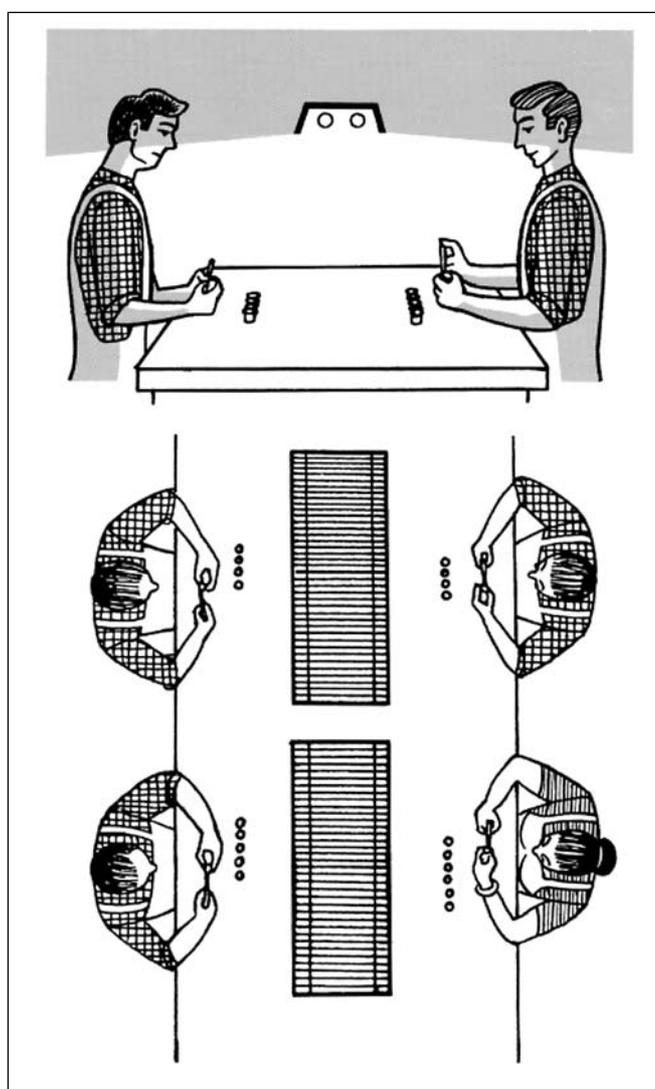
Prévoir des plafonniers horizontaux pour le travail avec de petits objets
